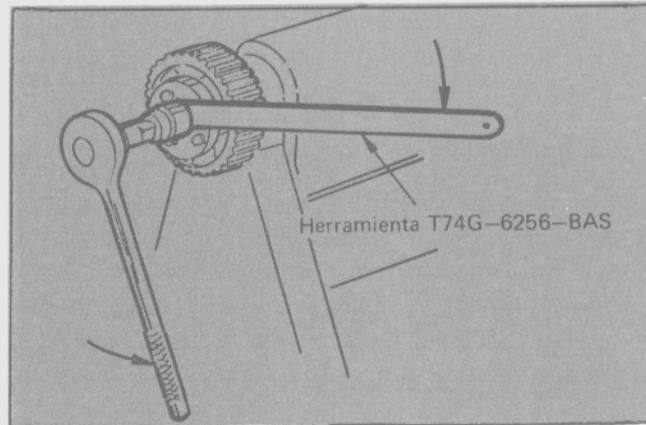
Colocación de la herramienta especial para extraer la rueda dentada.
